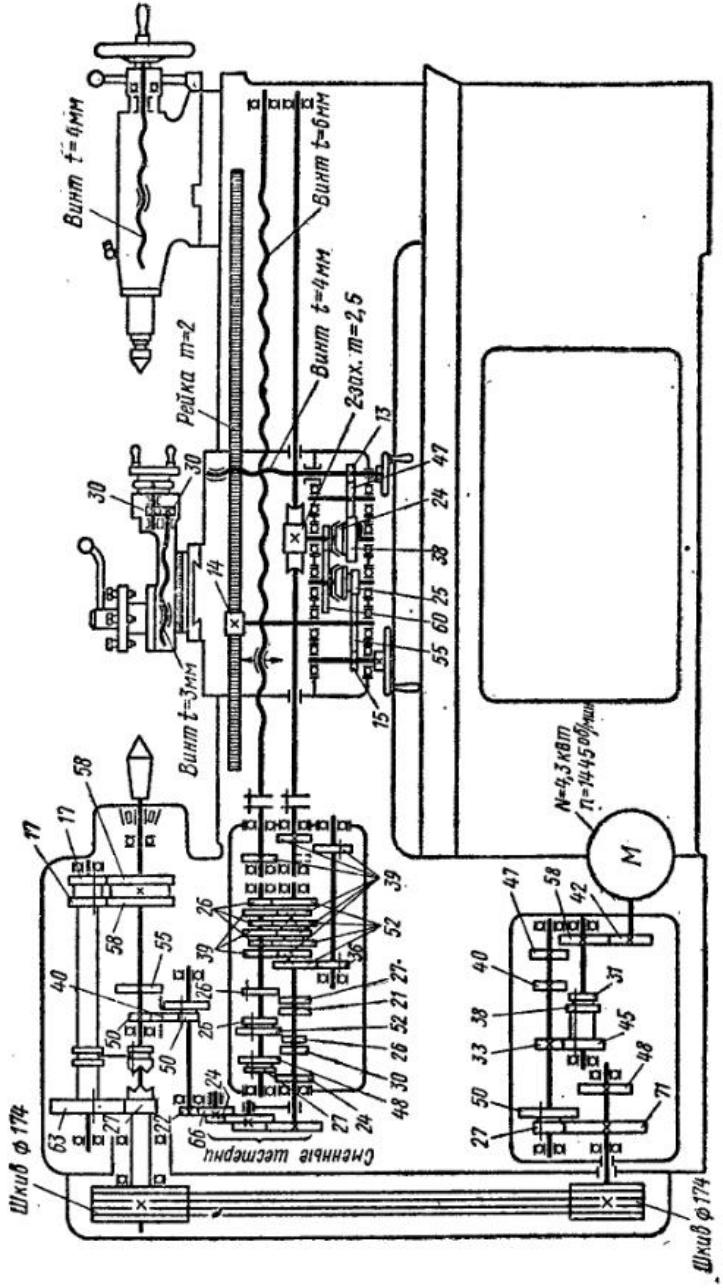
Кинематическая схема станка 1A62 (цифрами обозначены числа зубьев)
